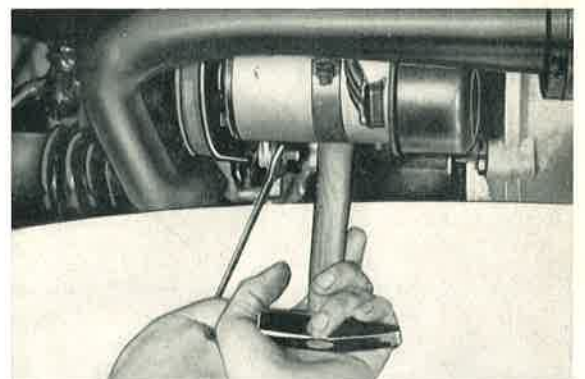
Die Befestigungsschraube an der Lasche wird bei vorgedrückter Lichtmaschine festgezogen.
